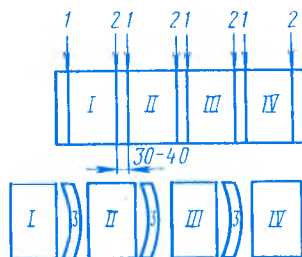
Вырезка без деформаций заготовок при резке двумя резаками:
